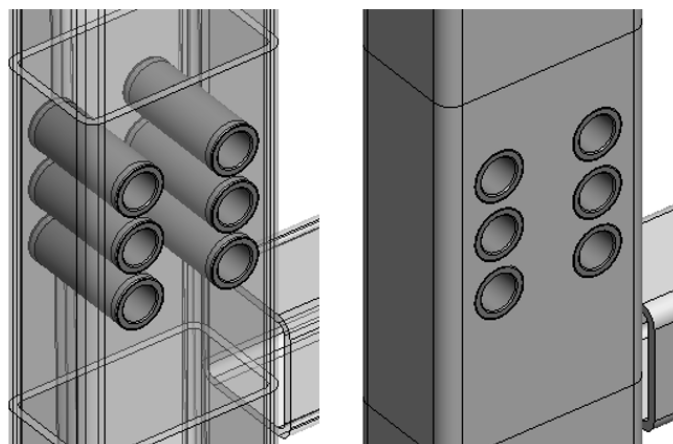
Tubos com roscado interior soldados ao quadro tubular.
